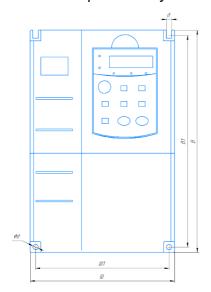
габаритные и установочные размеры устройств серии LCI в пластмассовом корпусе
